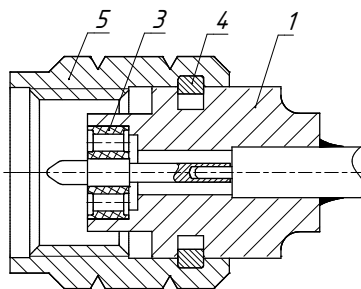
Установка накидной гайки на корпус кабельного соединителя
